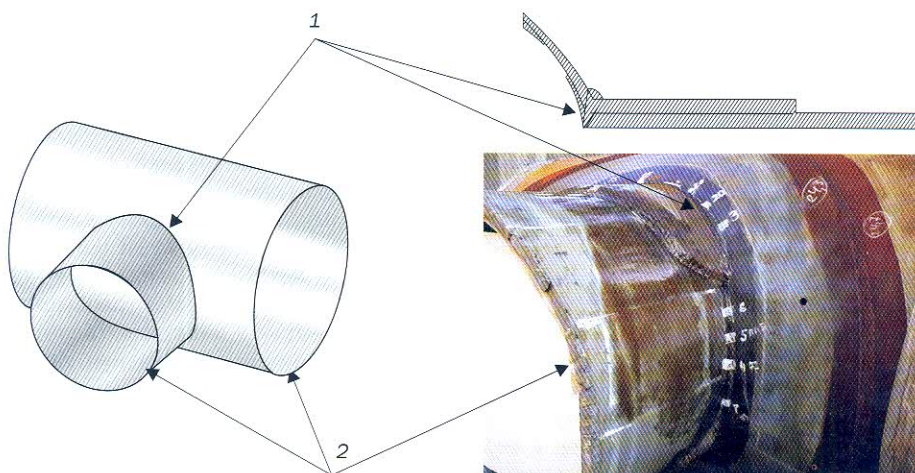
Объект контроля: 1 – внутреннее угловое сварное соединение приварки патрубка к обечайке (магистральной части) тройника; 2 – кольцевые стыковые сварные соединения приварки обечайки и патрубка тройника к газопроводу
